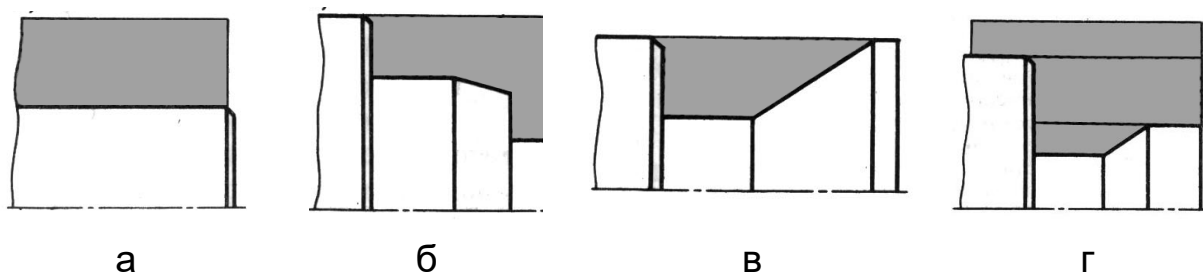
Поверхні, що утворюють контур деталі:
